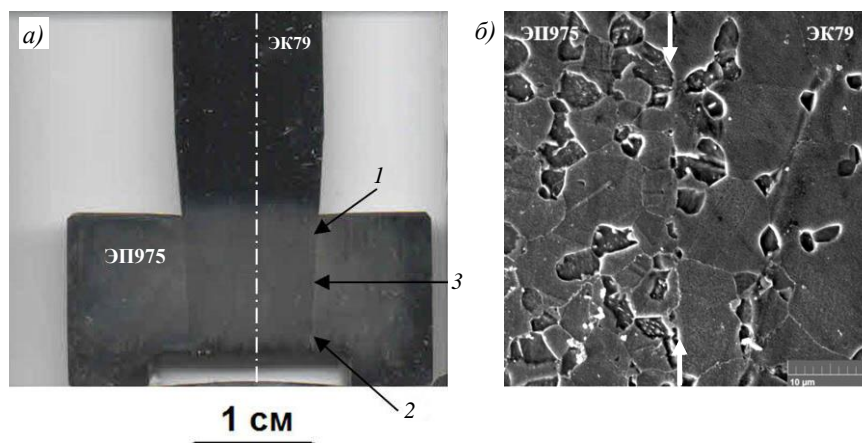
Образцы после сварки давлением: а – общий вид; б – структура в зоне твердофазного соединения [11]
